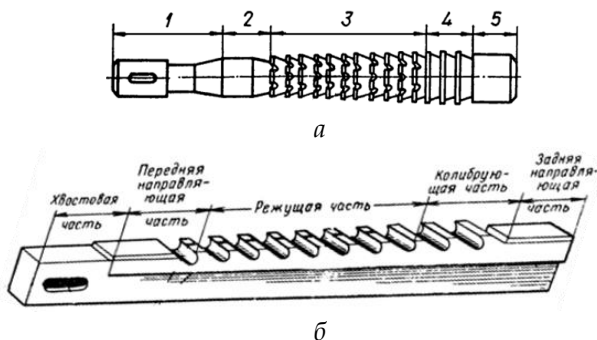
Основные конструктивные части протяжек для получения круглых отверстий (а) и шпоночных пазов (б):
